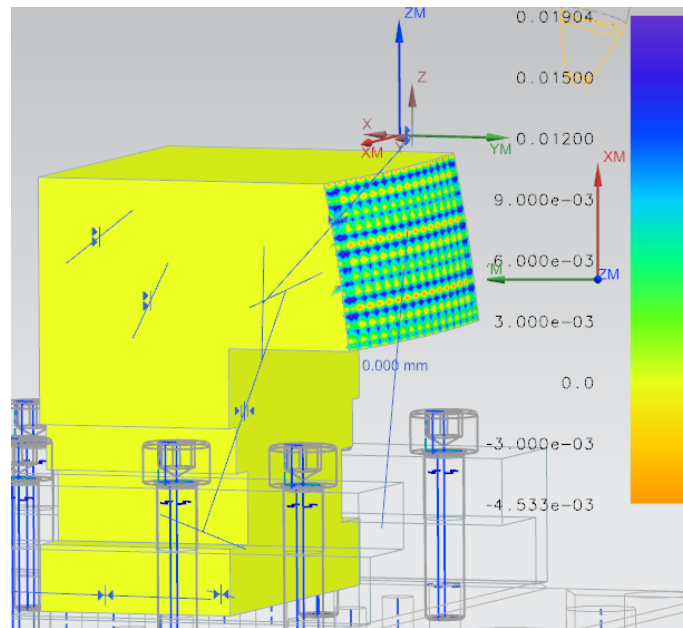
Analýza zbytkového materiálu po obrobení soudečkové frézy R85
